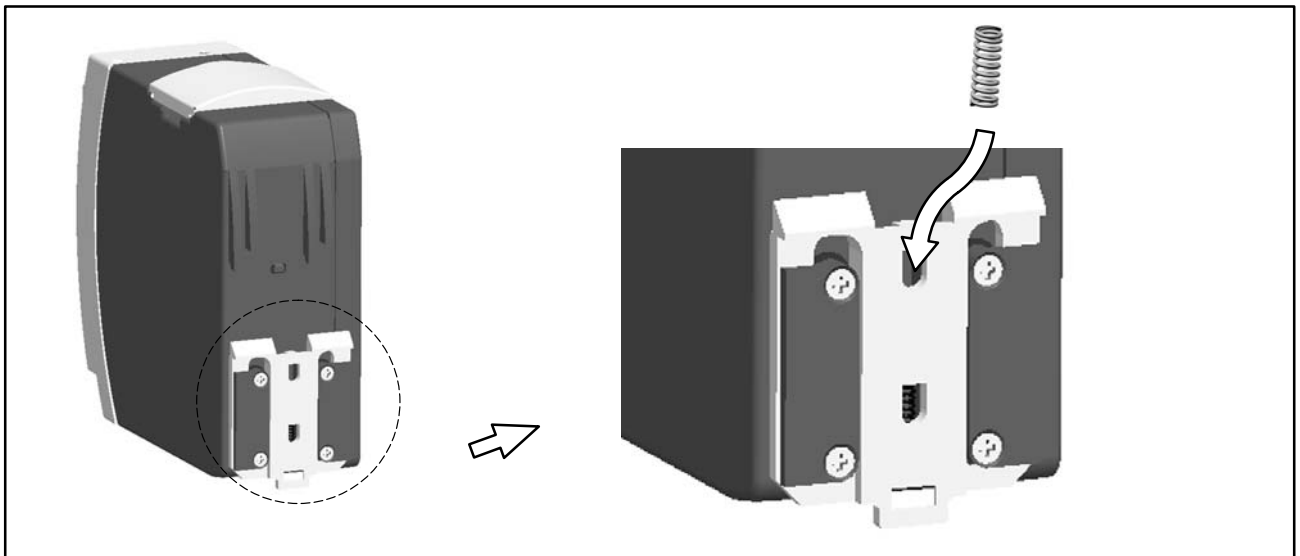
Inserzione di una seconda molletta per il più stabile fissaggio del modulo sulla guida portante
